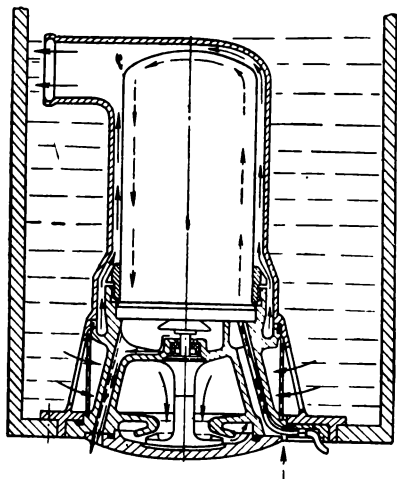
Кессонный ЭЦН с нижним расположением рабочего колеса
